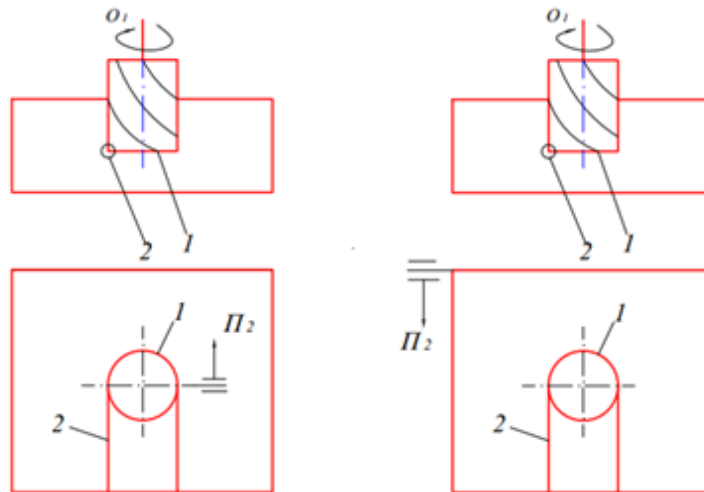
Фрезеруванні пазу кінцевою фрезою
